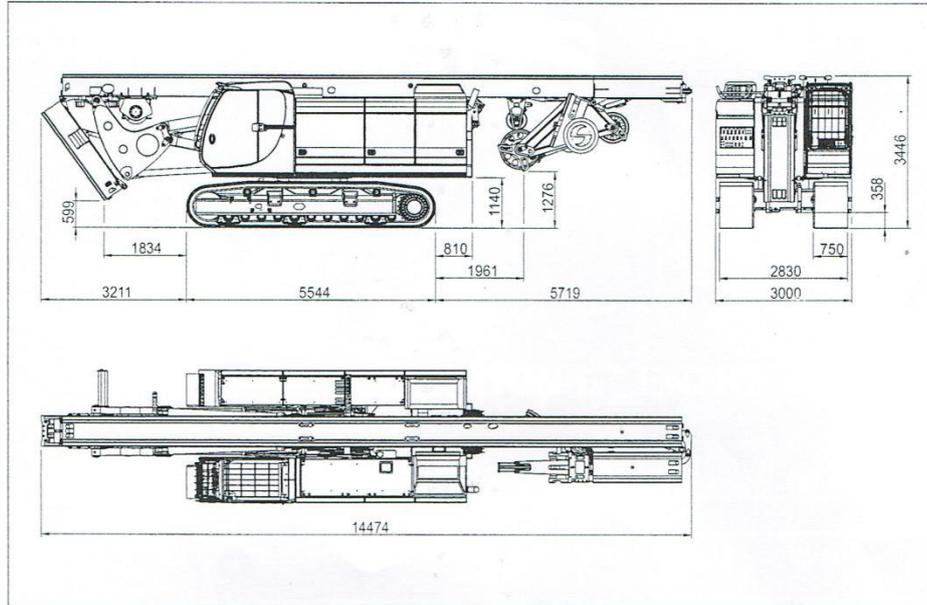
Dimensions de la machine en condition de transport sans table de rotation et pied du mât (mm)
